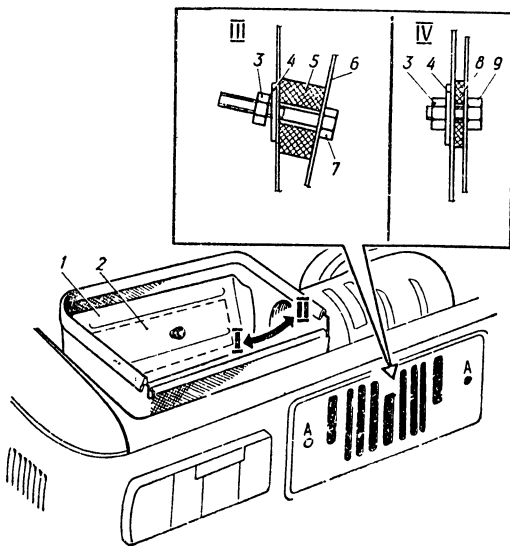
Воздуховод охлаждения двигателя и крепление заднего номерного знака:
